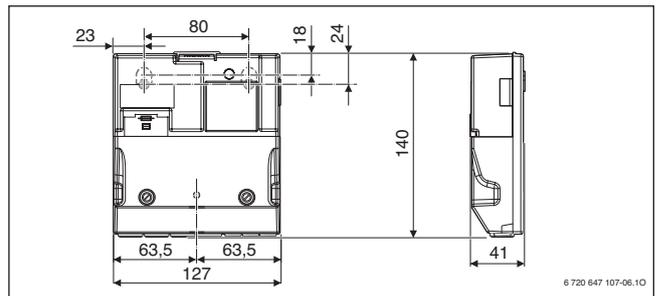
Abmessungen Solarmodul SM50 bei Installation an der Wand (Maße in mm)
